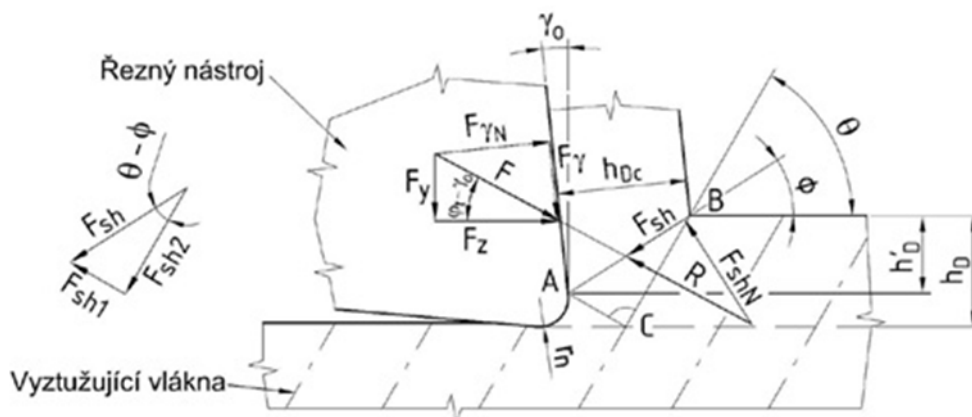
Frézování kompozitu speciální válcovou frézou [16].
